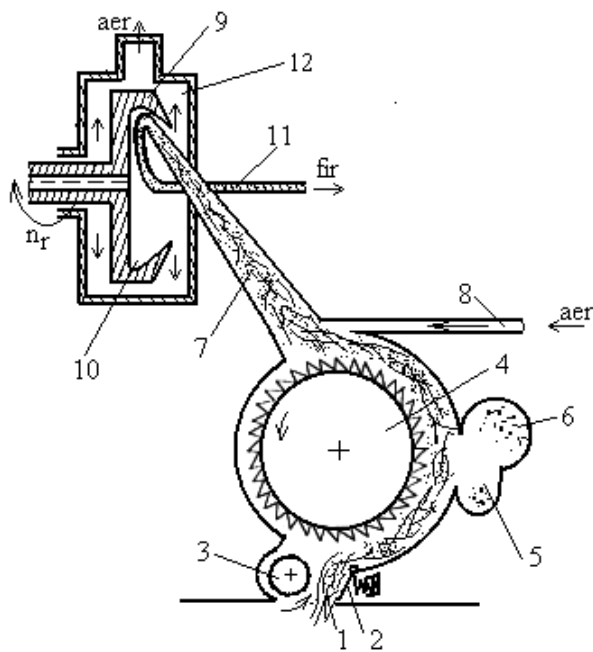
Principiul mașinilor de filat cu rotoare
